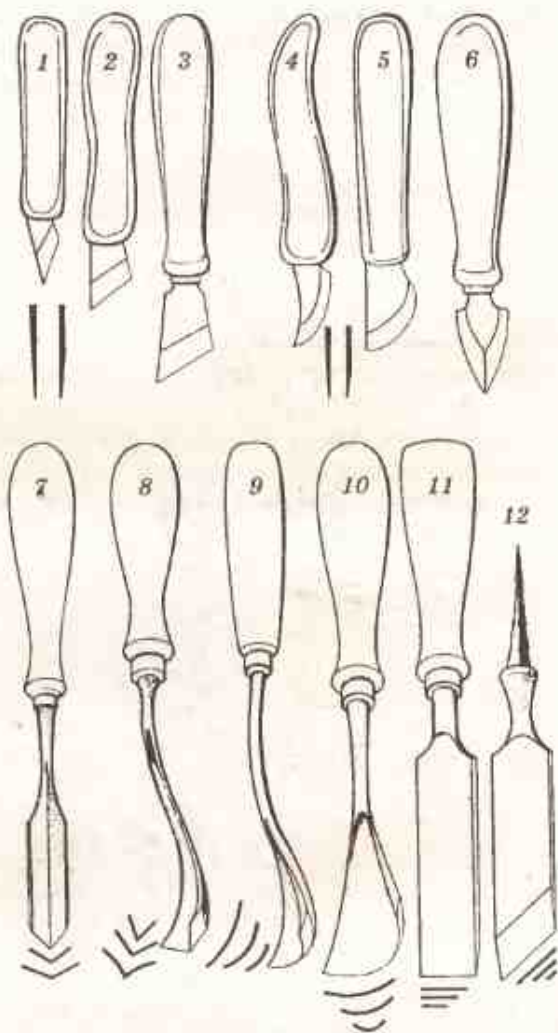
Инструмент для геометрической резьбы: 1—3 ножи-косыки; 4—6 ножи-резак; 7, 8 — стамески-уголки; 9 — полукруглая стамеска; 10 — отлогая стамеска; 11 — прямая стамеска; 12 — стамеска-косык.
